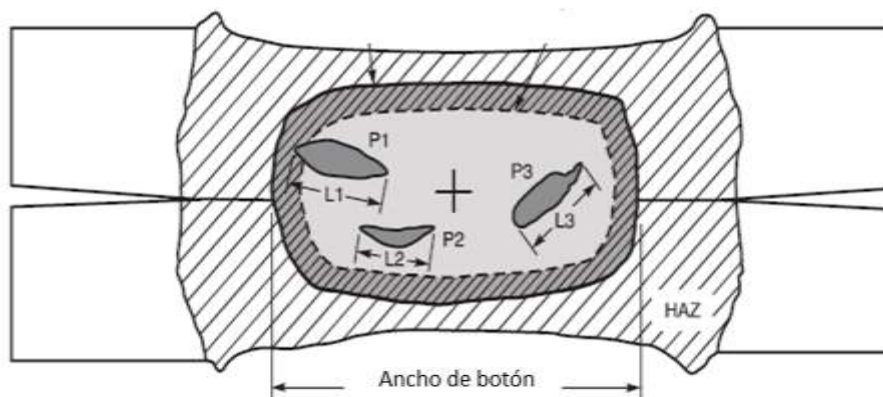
Representación de la porosidad presente en botones de soldadura RSW [22].
